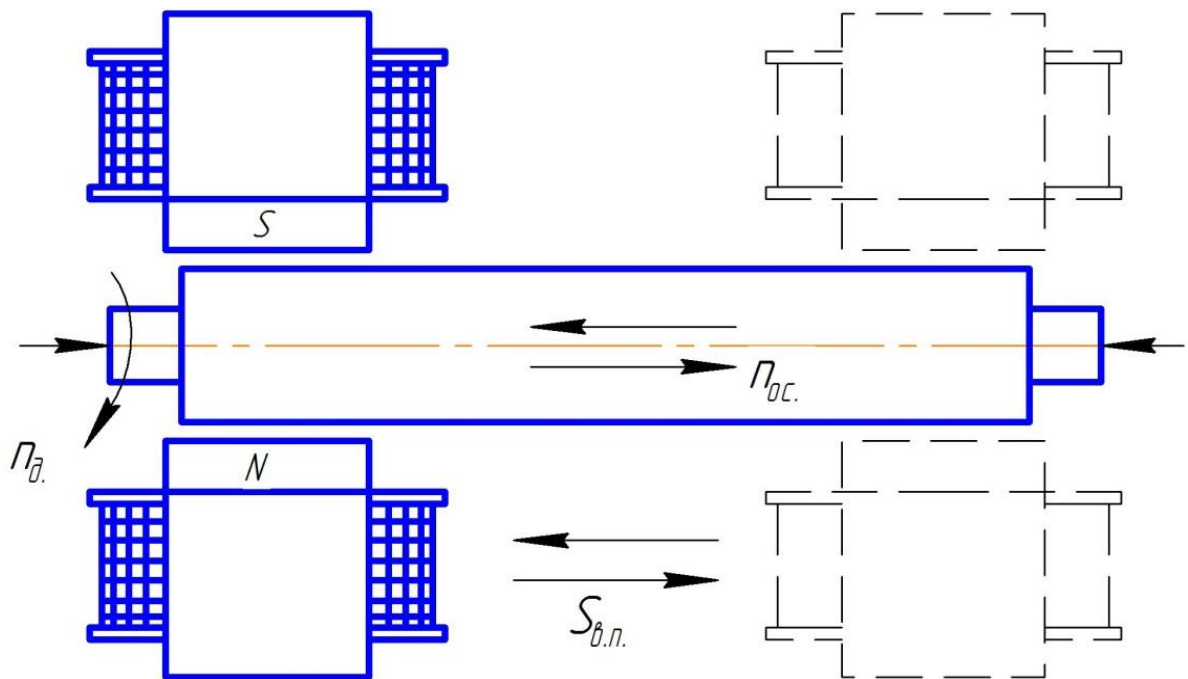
Схема зовнішнього циліндричного (круглого) полірування поверхонь
